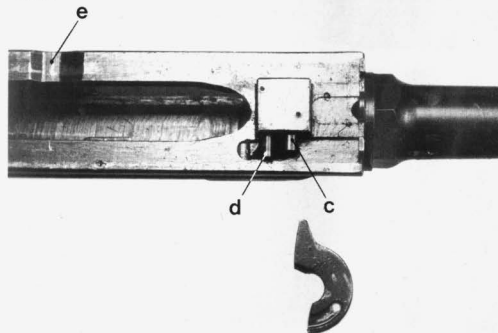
Der ausgebaute Beschleuniger der schwedischen M/40. c = federnder Führungsstift, d = eingepreßter Anschlagstift, e = Steuerkurve für den Unterbrecher.
